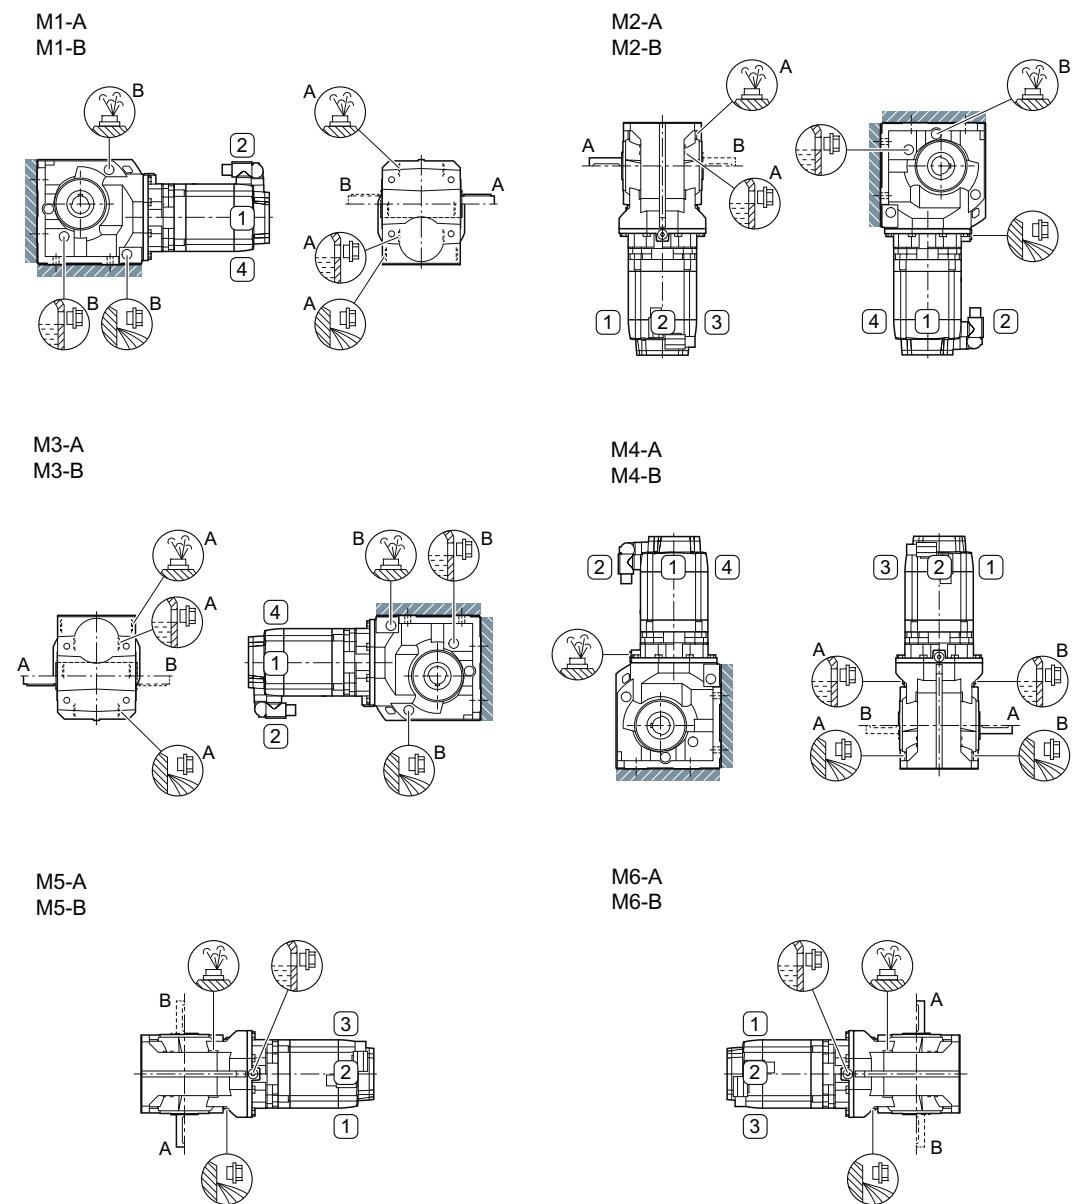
Einbaulagen für Servo-Stirnradschneckengetriebemotor C, Fußausführung, Baugrößen 49 - 89, 2-stufig
